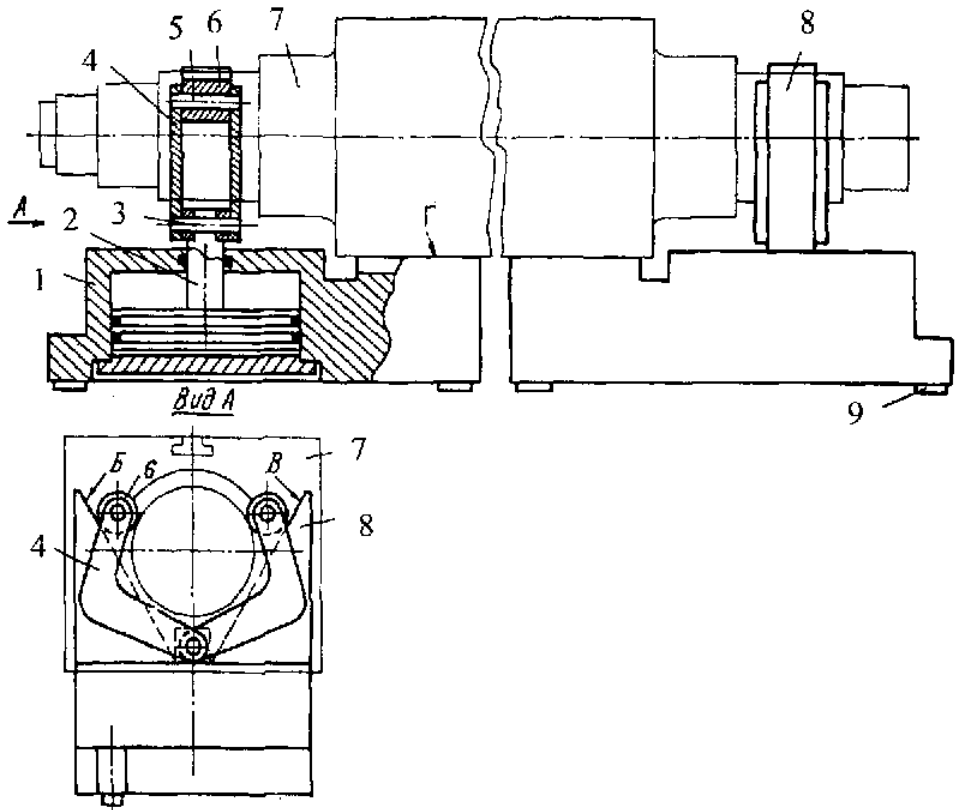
Пневматичний пристрій для закріплення заготовок типу „валик”
